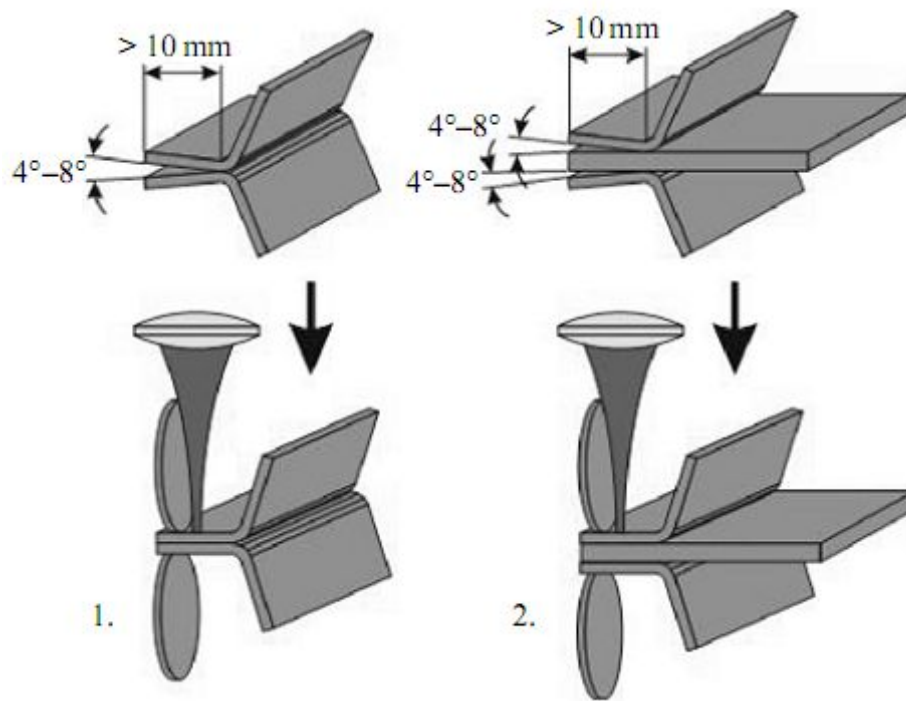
Схематическое изображение узла сварочного автоматического оборудования
